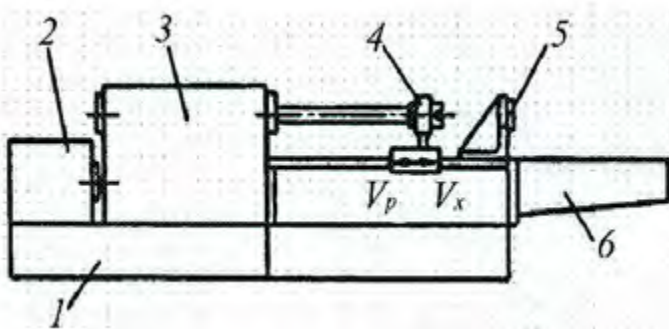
Загальний вид горизонтально-протяжного верстату
